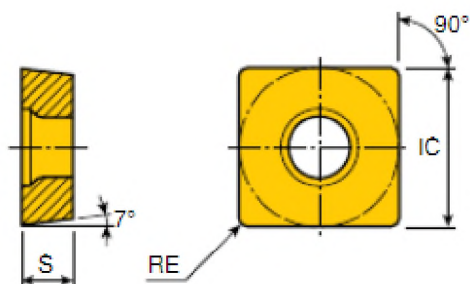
Пластина SCMT09T308FG . CVD покриття : TT8125B
